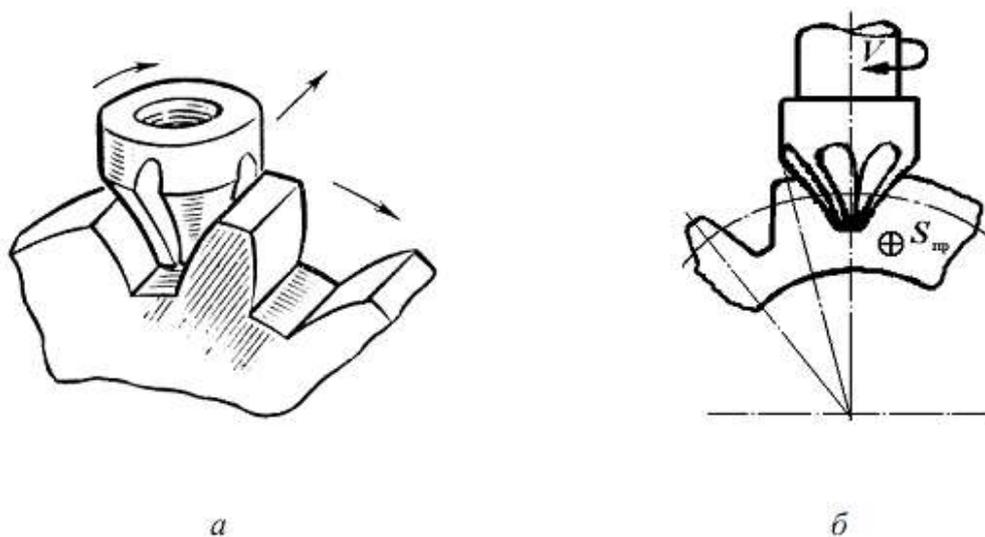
Обработка зубчатых колес модульными пальцевыми фрезами
